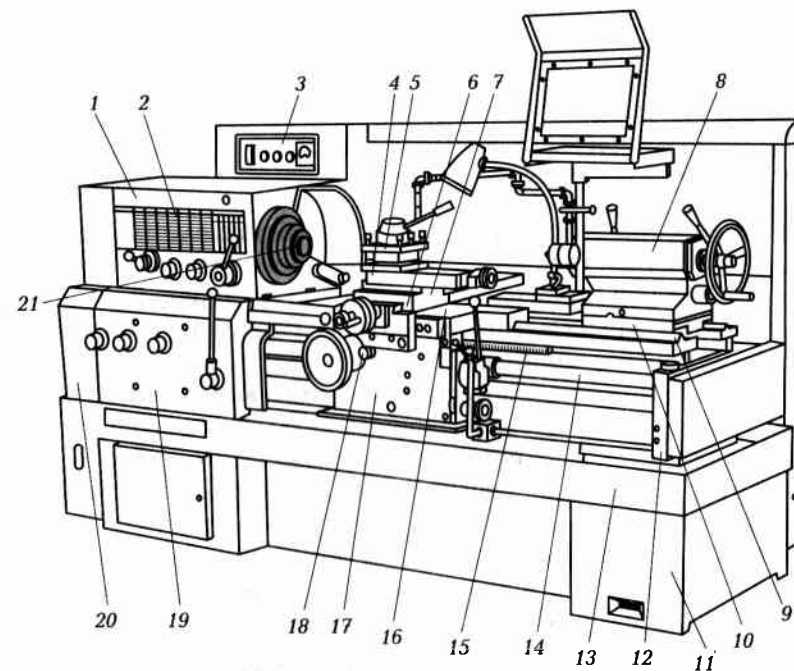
Сборочные единицы токарно-винторезного станка мод. 16К20
